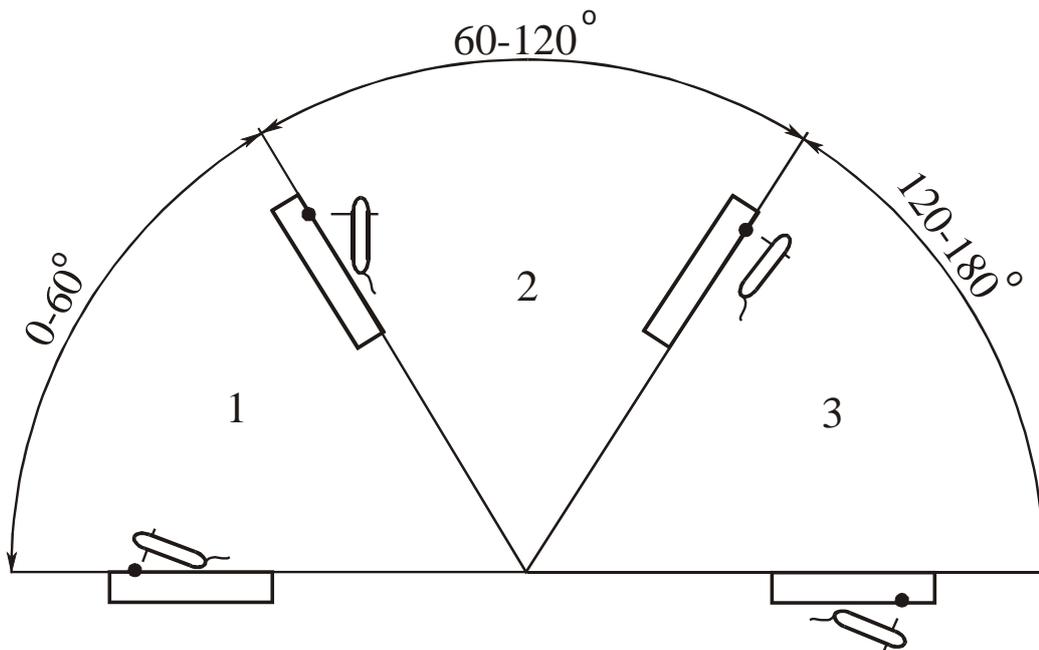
Расположение сварного шва в пространстве: 1- нижнее; 2- вертикальное или горизонтальное; 3- потолочное.
